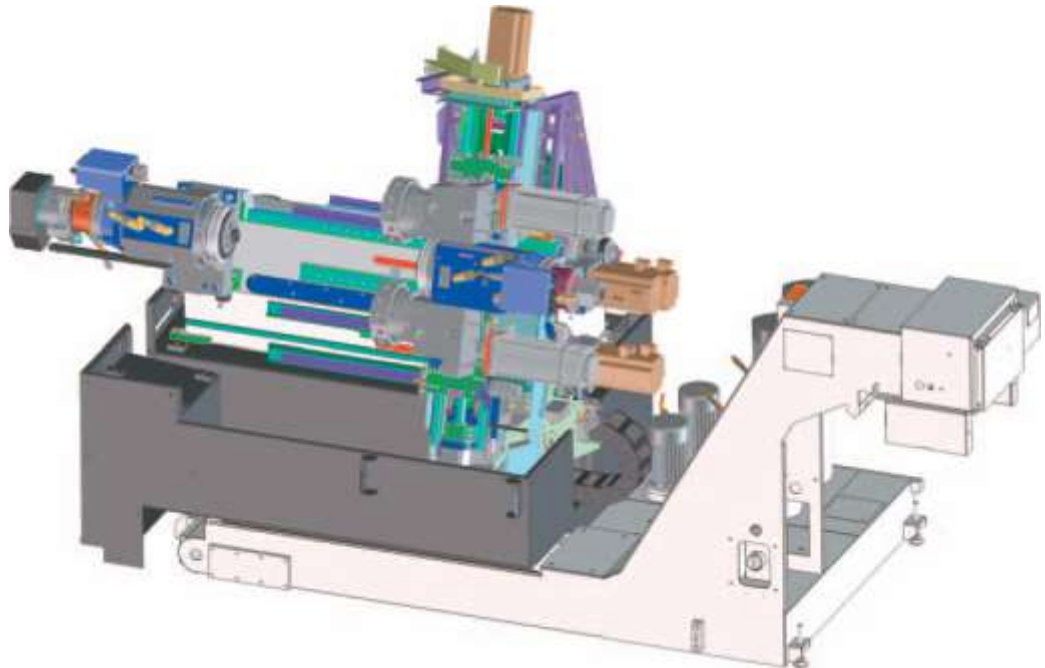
Компонівка серії токарних верстатів з ЧПК HYPERTURN фірми EMCO для багатоінструментальної обробки
